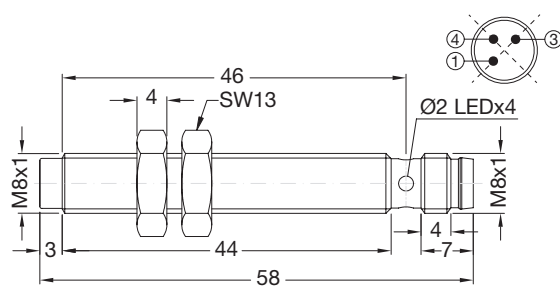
Lange Ausführung, Nicht bündiger Einbau, Steckversion
